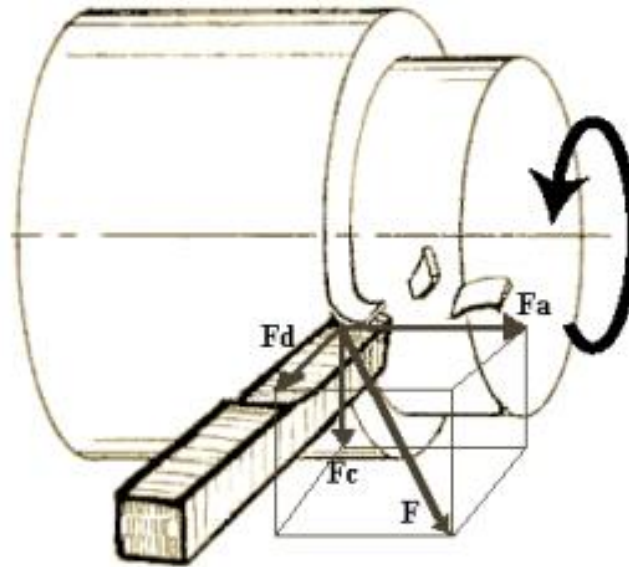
Esquema de fuerzas actuantes durante un proceso de arranque de viruta.
